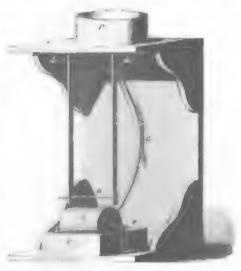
Bummirapparat fur Popier ofine Enbe.
